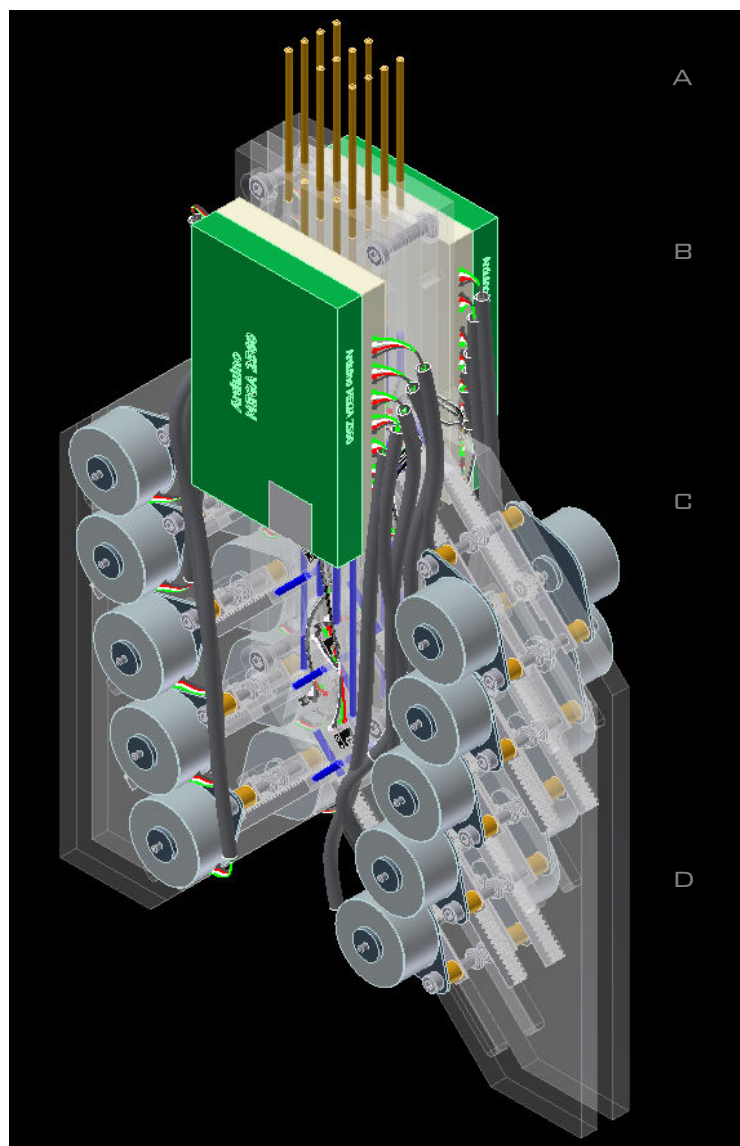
Reactive Shape Display. Gesamtansicht des CAD-Entwurfs. (A) Stifte (B) Arduino-Mikrocontroller mit Shield (C) Motoren mit Ritzeln und Zahnstangen (D) Gehäuse mit Fräsungen bzw. Bohrungen.
